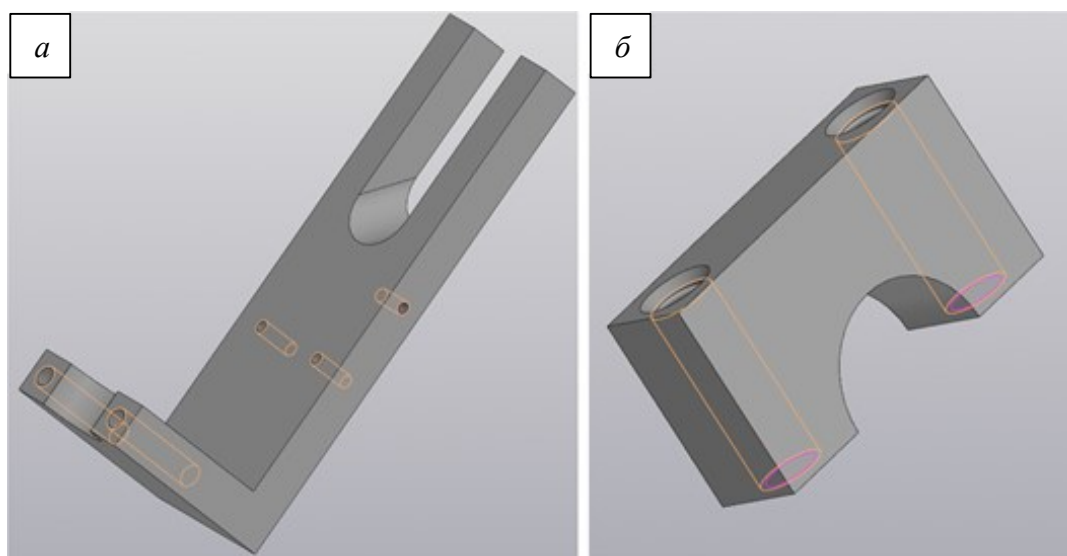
3D модель держателя для крепления сварочной горелки (а), фиксатор сварочной горелки (б)
